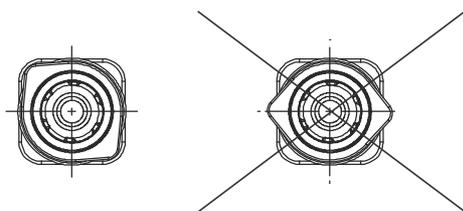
Instalar o O-ring sobre a parte fixa do empanque.
